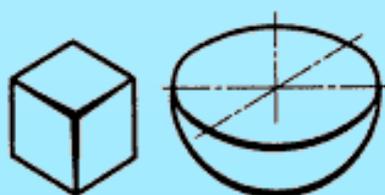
Условный чертеж детали — толщина линий в чертежах
